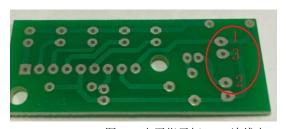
电平指示灯 PCB 连线点两个 PCB 连接后如图所示:
